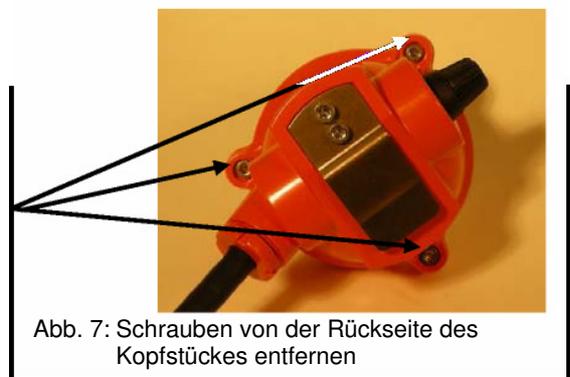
Schrauben von der Rückseite des Kopfstückes entfernen
